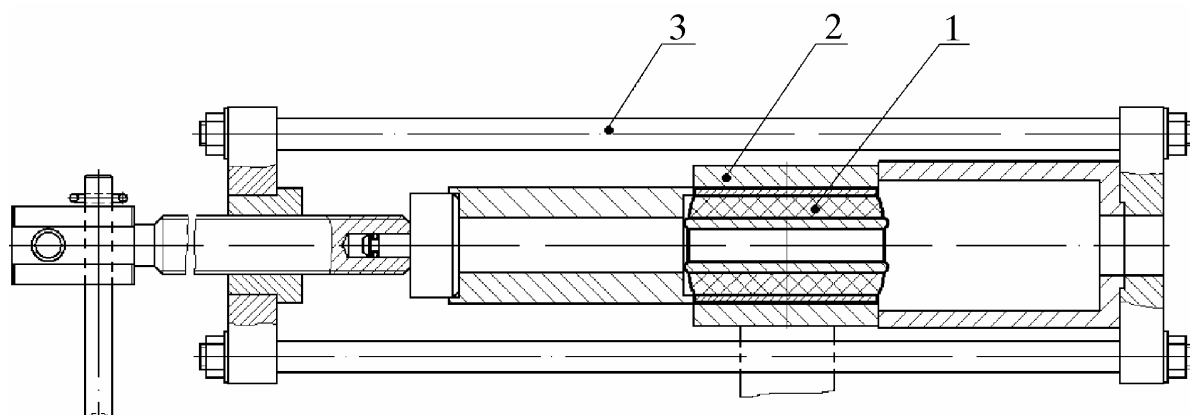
Выпрессовка резинометаллического шарнира из наконечника штанги стабилизатора:
